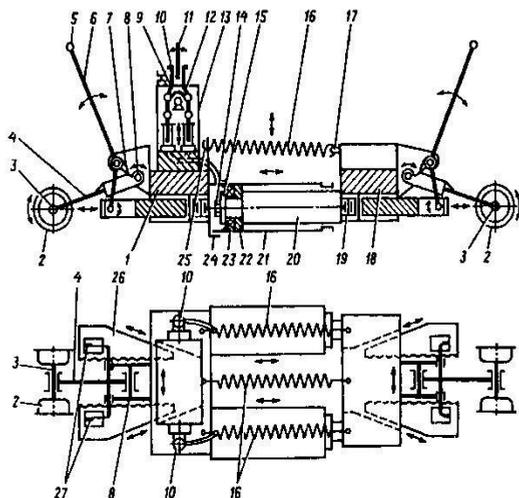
Структурная схема гидравлического разгонщика РН-01А: 1, 18 – корпуса разгонщика; 2 – ролик; 3 – ось ролика; 4 – кронштейн; 5 – поперечина рукояти; 6 – рукоять; 7 – запорная собачка; 8 – ось кронштейнов; 9 – подшипник вала; 10 – втулка для рукояти; 11 – рабочая рукоять; 12 – коромысло; 13 – масляный резервуар; 14 – винт; 15 – нажимное кольцо; 16 – возвратные пружины; 17, 25 – внутренние ребра корпусов; 19 – болт; 20 – поршень; 21 – распорный цилиндр; 22 – направляющее кольцо; 23 – резиновая манжета; 24 – крышка цилиндра; 26 – зажимной клин; 27 – поводки
